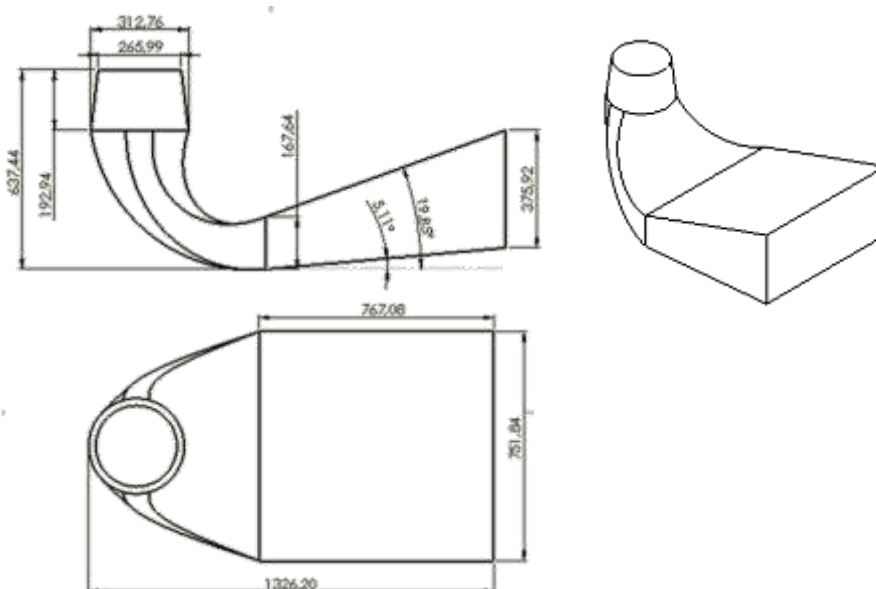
Vista alzado, planta e isométrica con las dimensiones del tubo de aspiración.
